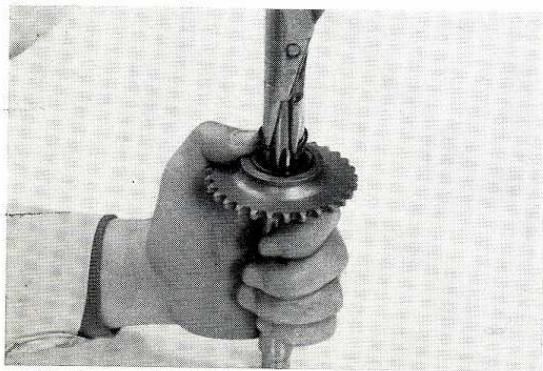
DEMONTAGE DE L'AXE DE PEDALES.
